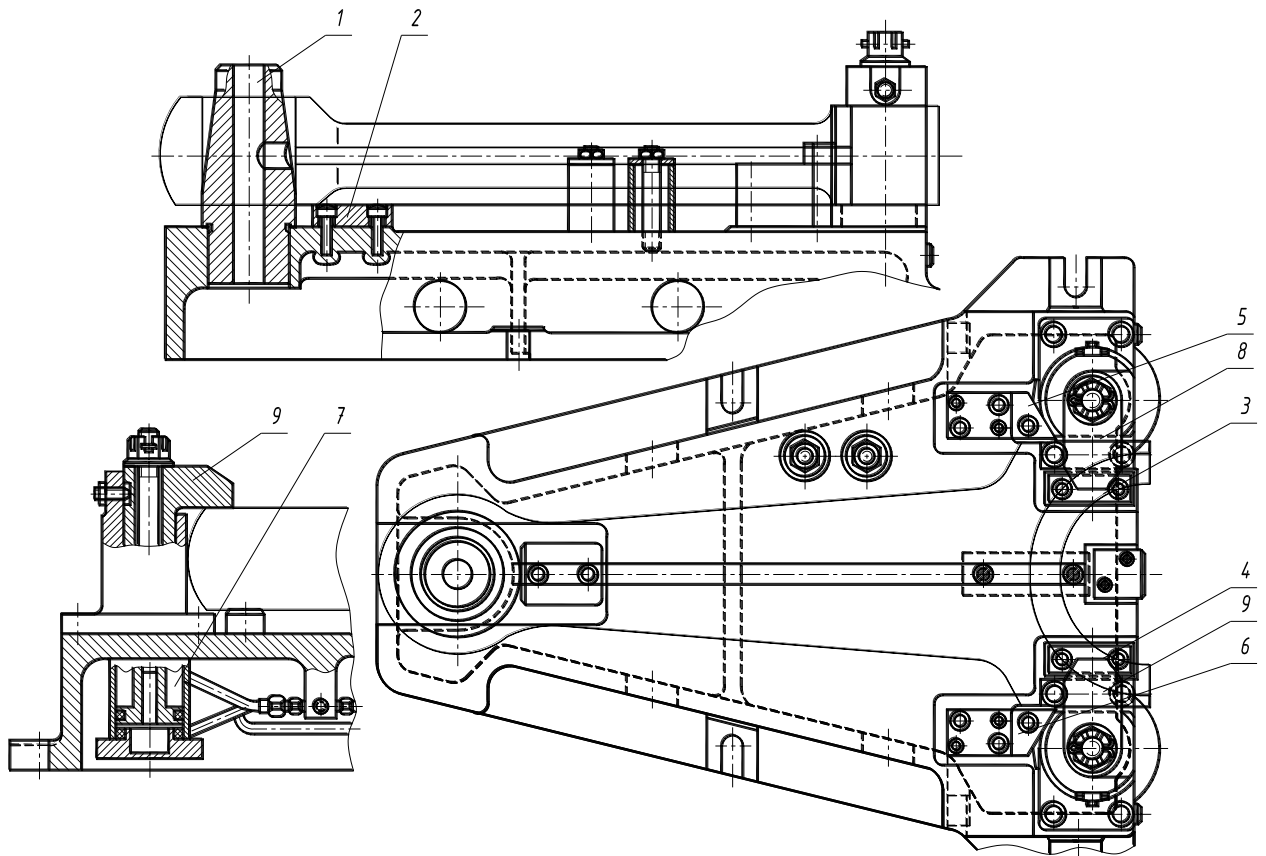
Приспособлення для закріплення деталі при фрезерованні пазів у шатуні й кришці шатуна під вкладиші
